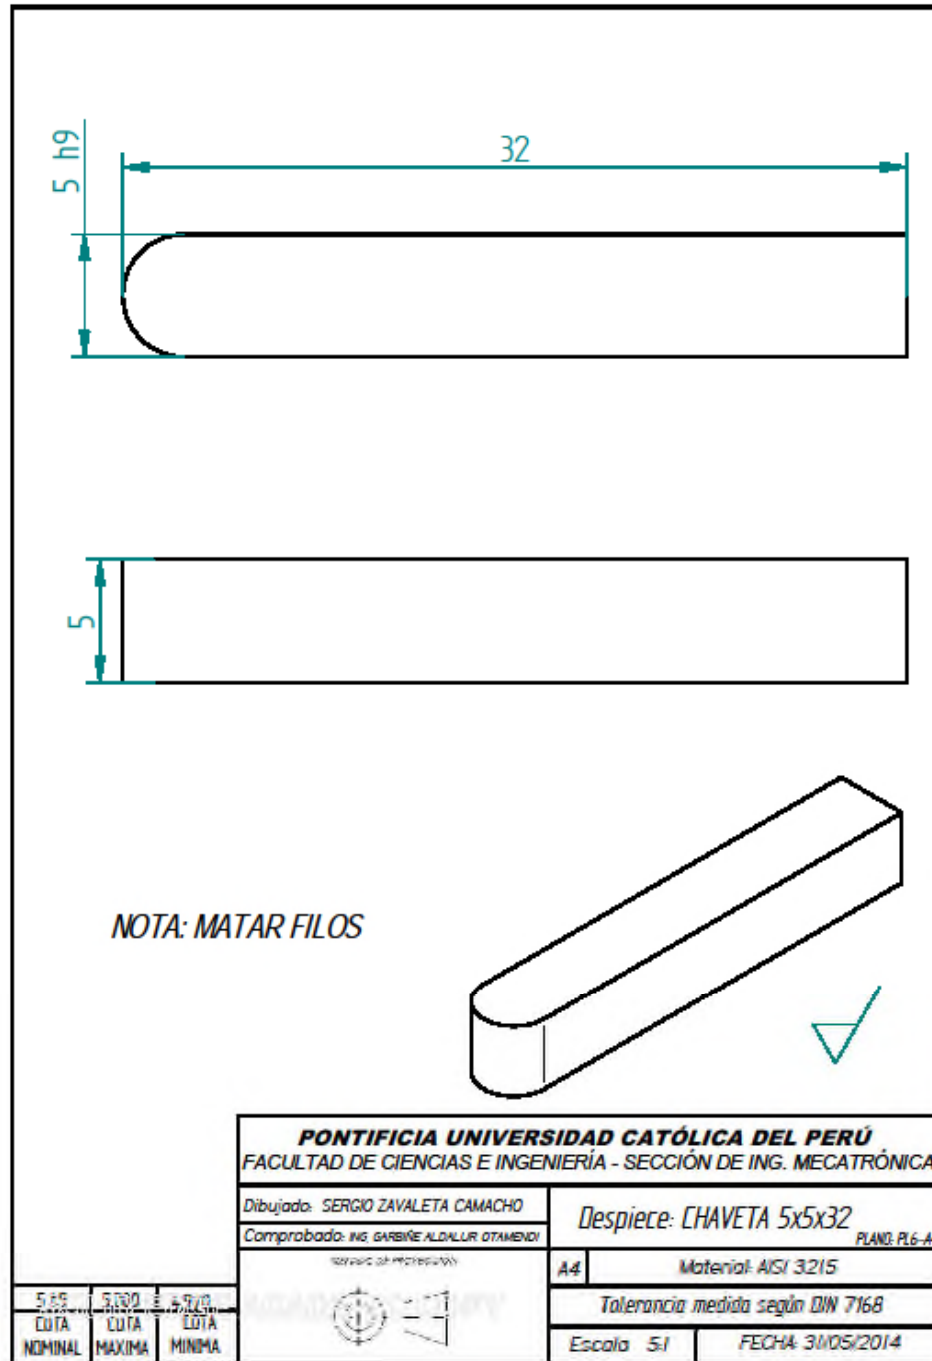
Plano de despiece de la chaveta del engranaje E1. Fuente: Elaboración propia.
